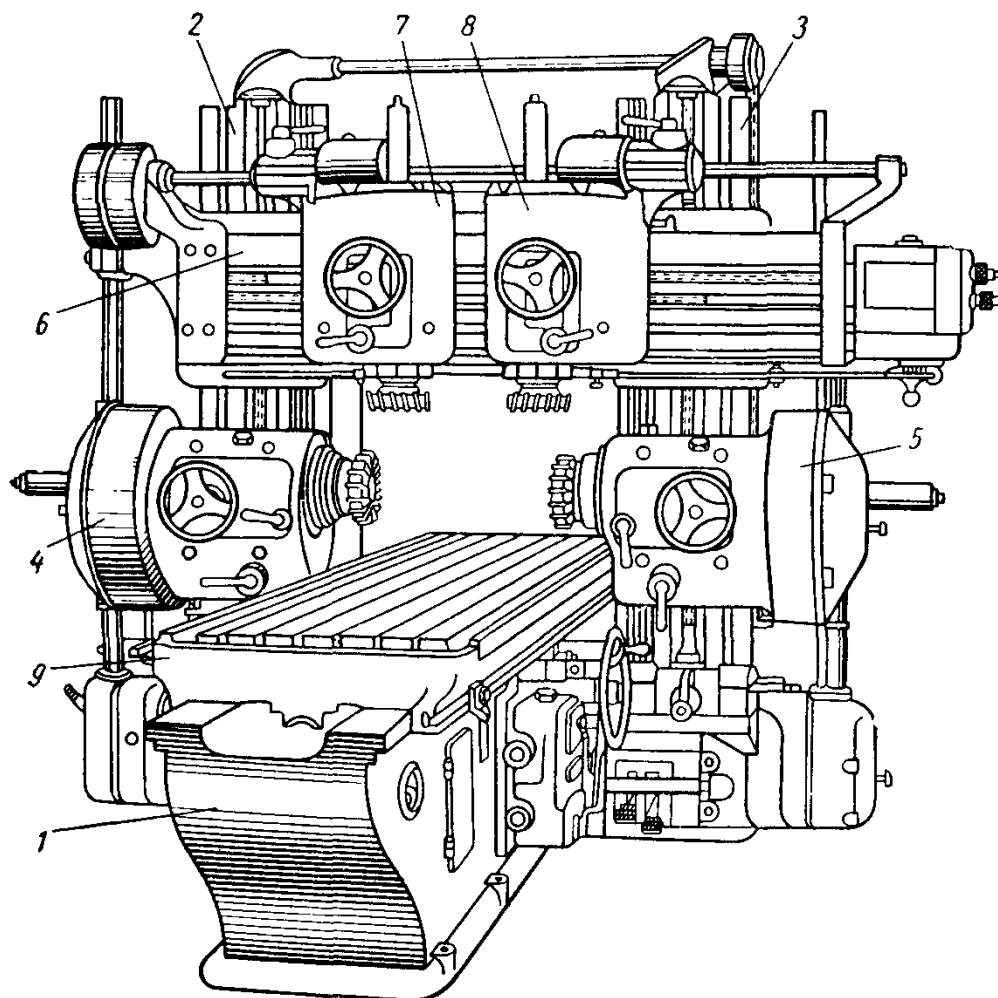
Поздовжньо-фрезерний верстат
